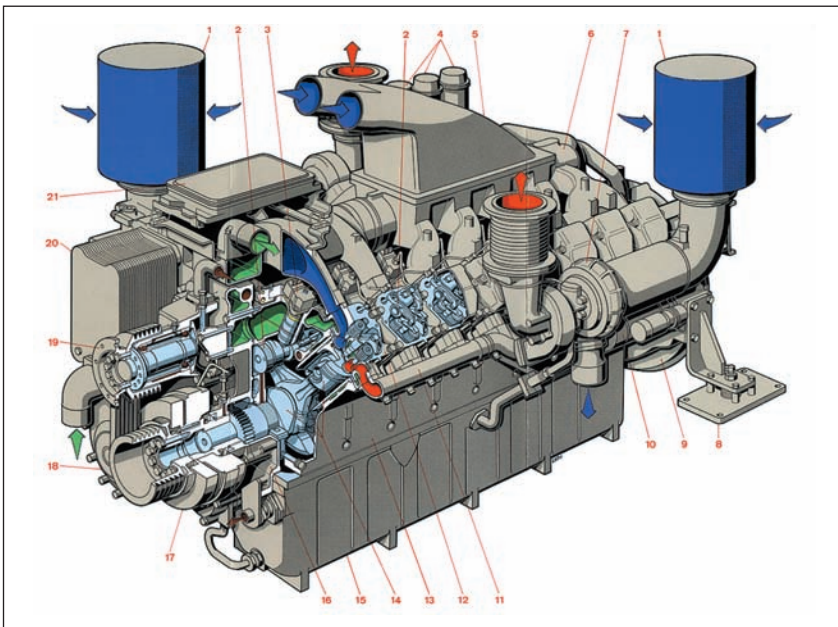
Ausführungsbeispiel für einen Aggregatmotor (MTU 16V 2000 G.2)
